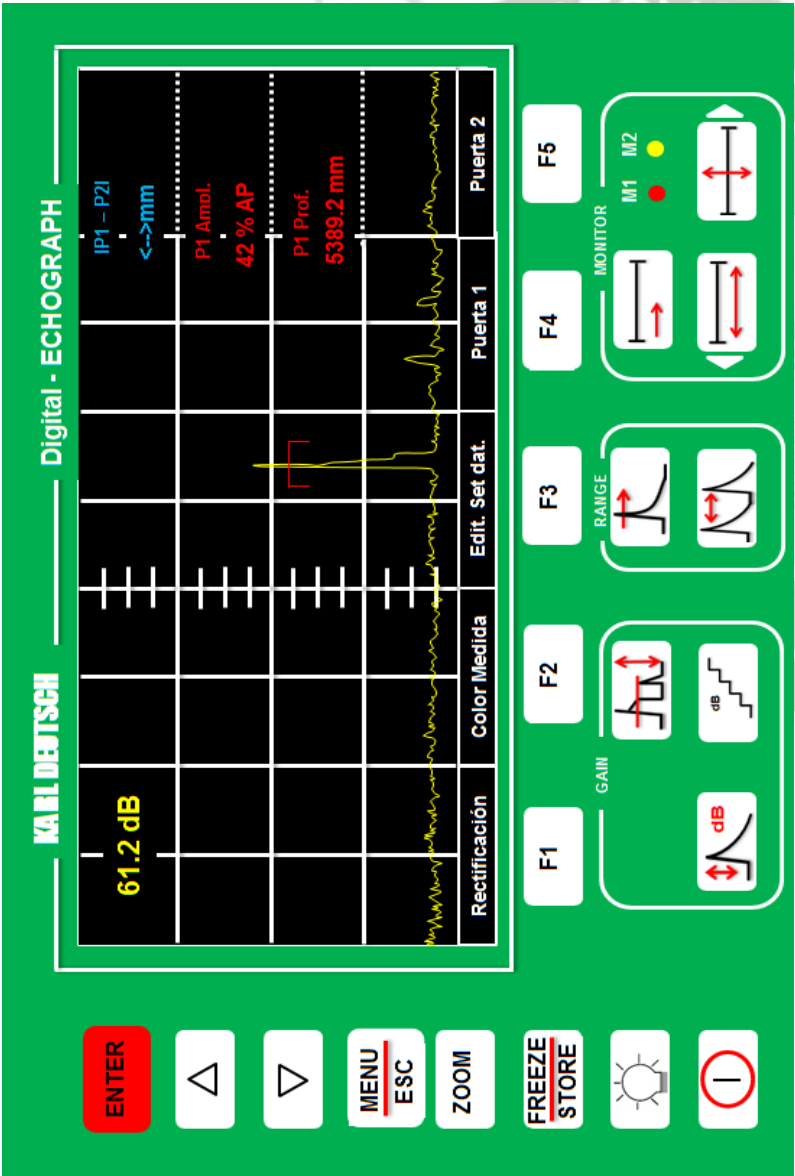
Pantalla de Inspección 1 lado izquierdo Fuente SPCC
